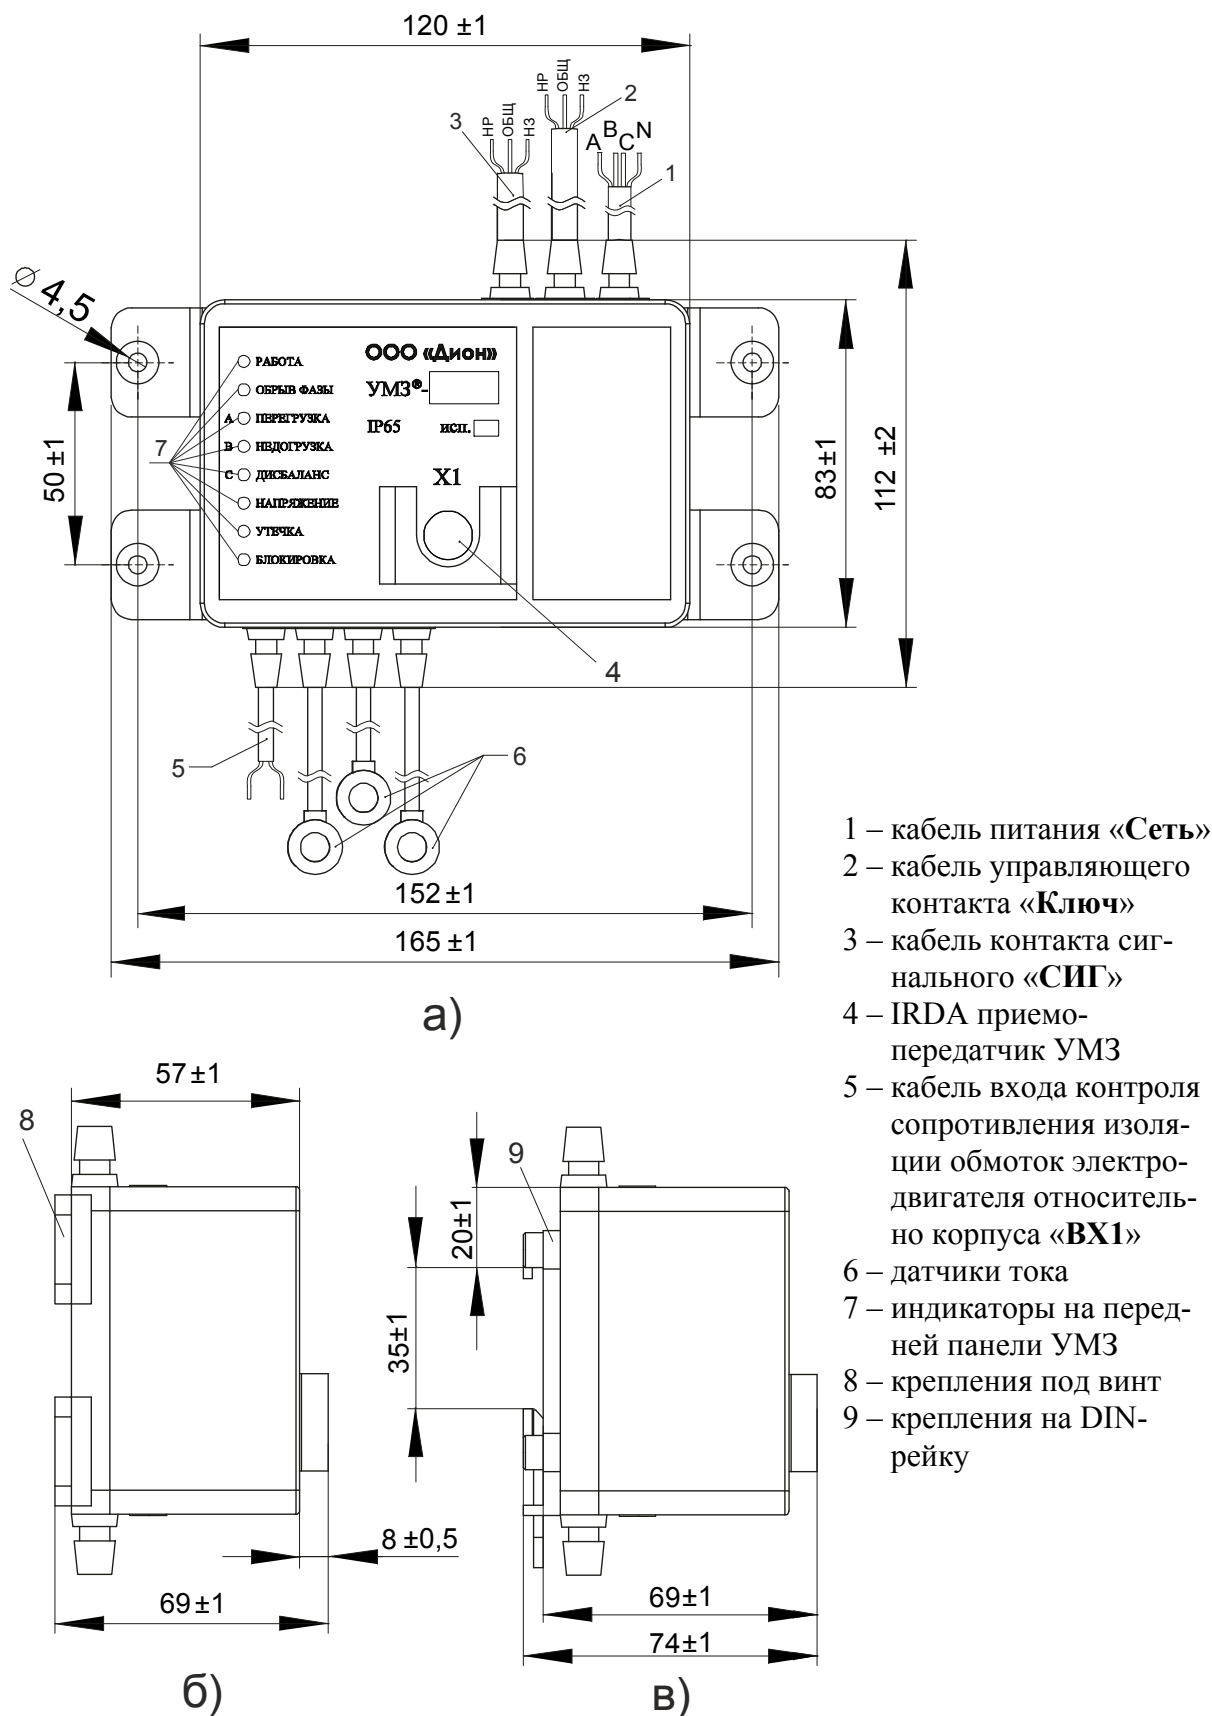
Внешний вид и габаритные размеры устройства УМЗ. (а – вид спереди устройства УМЗ с установленными креплениями под винт; б – вид слева устройства УМЗ с установленными креплениями под винт; в – вид слева устройства УМЗ с установленными креплениями на DIN-рейку.)
